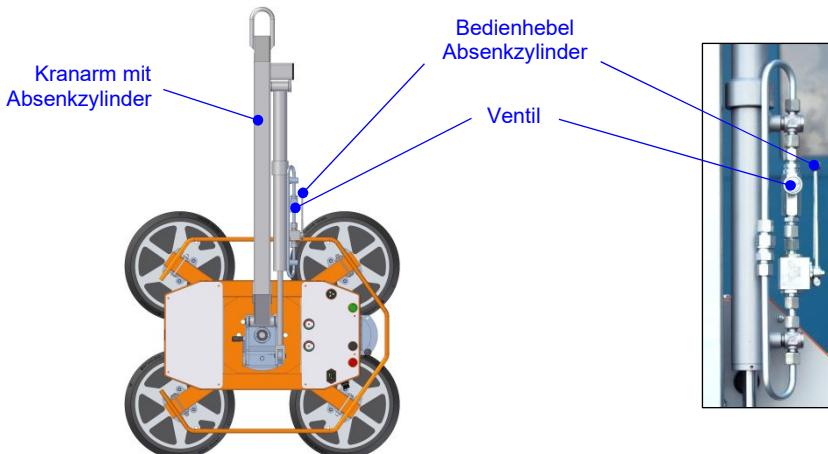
Kranarm mit hydraulischem Absenkzylinder
